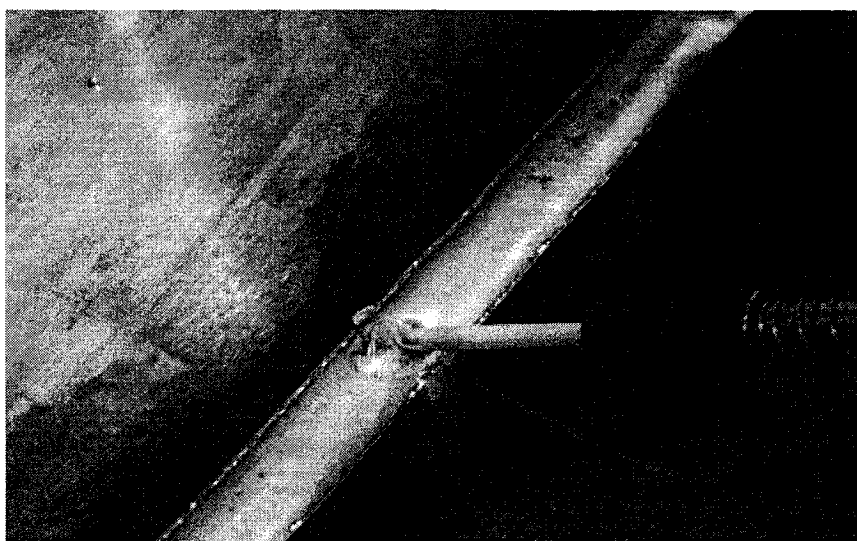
Thermocouple « harpon » T16 dans le cordon de soudure
